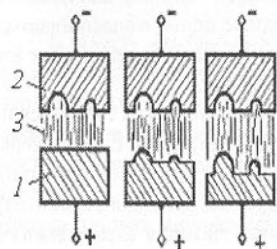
Схема анодно-гидравлической размерной обработки изделия (копирования профиля)
